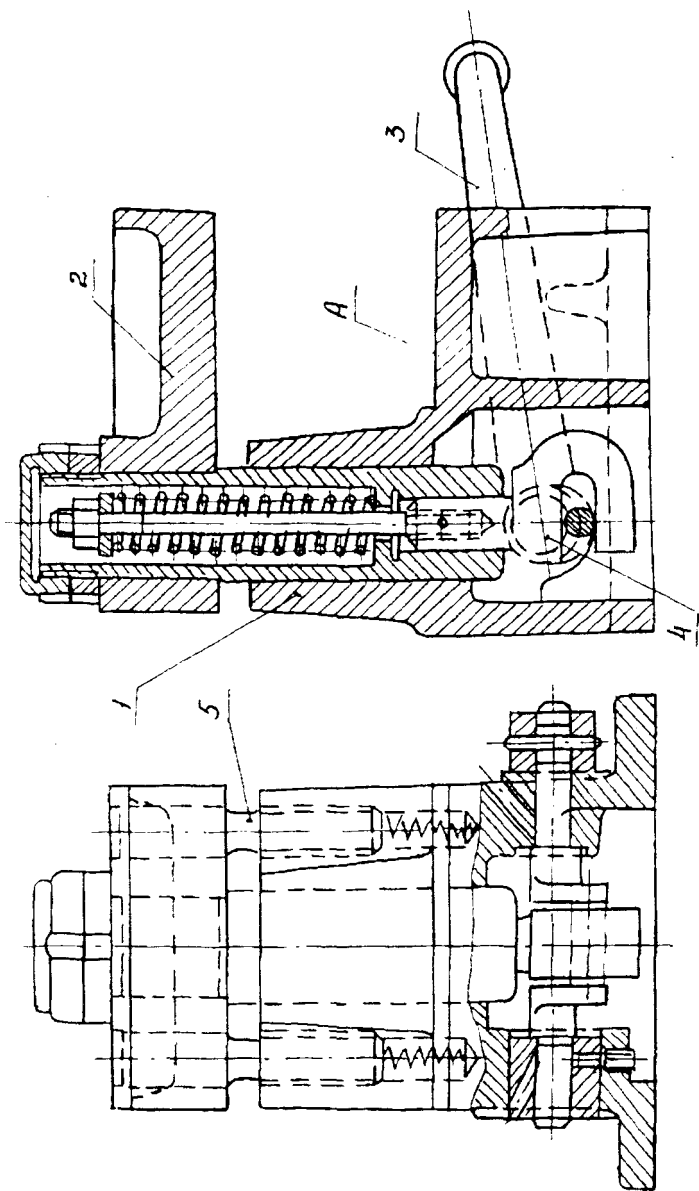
Стандартизованная базовая сборочная единица скальчатого кондуктора
